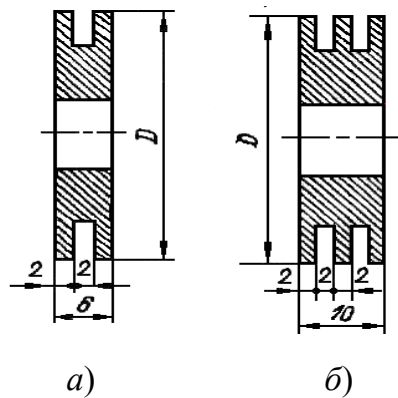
Эскизы дисков металлических для предварительной правки шлифовальных инструментов: *а* – одной канавкой; *б* – двумя канавками
